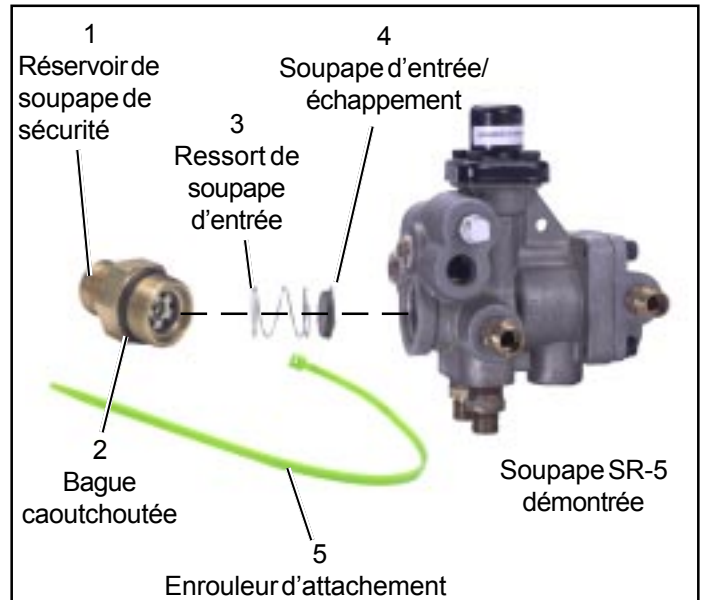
Trousses de modification d'assemblage et de désassemblage
